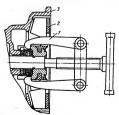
Схема демонтажа крыльчатки: 1— съемник; 2— крыльчатия; 3— корпус подмининков масоса
